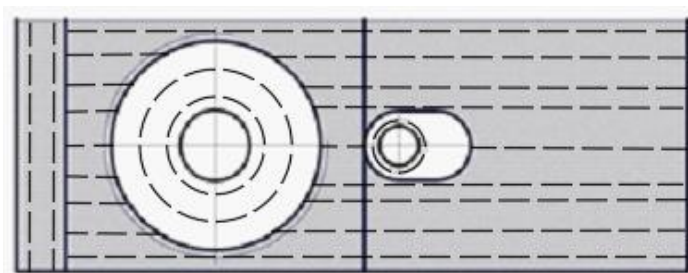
Схема сканирования корпуса затяжки-делителя
